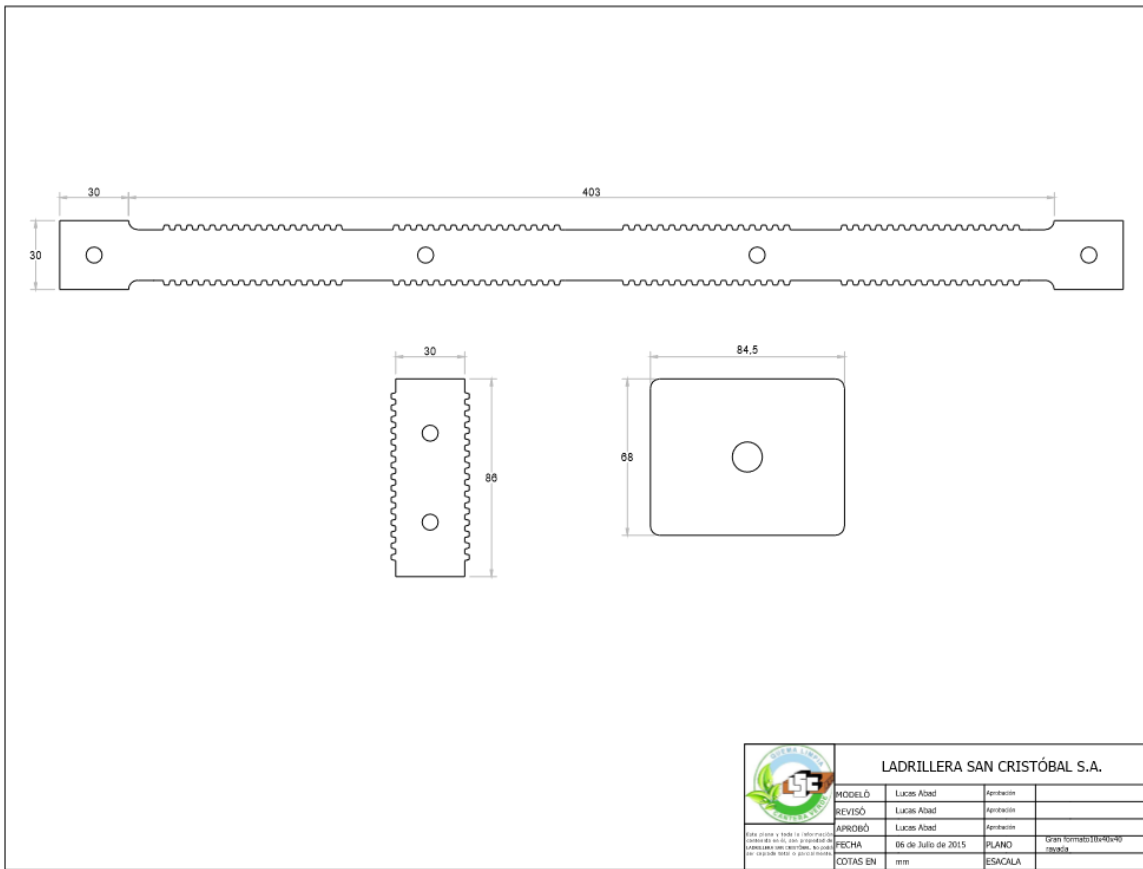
Despiece de los componentes del diseño del molde empleado para la fabricación de piezas gran formato.
